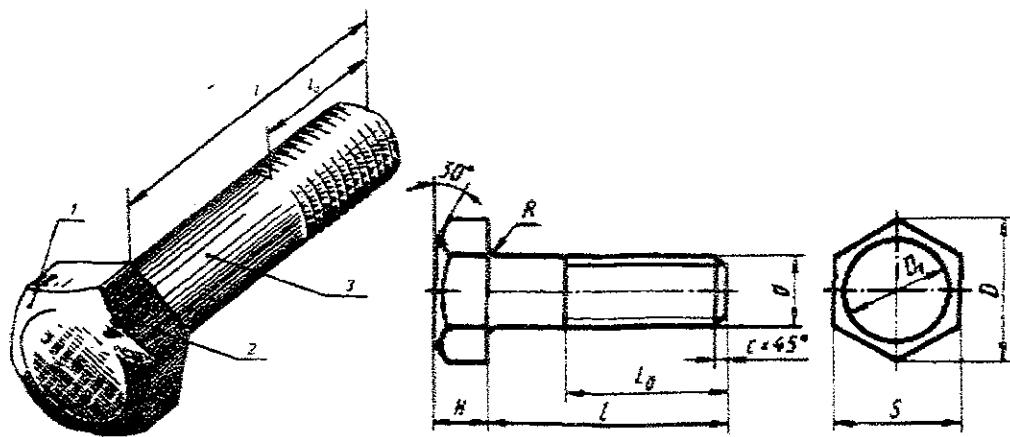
Элементы болта: 1 – фаска; 2- головка; 3 – стержень;
